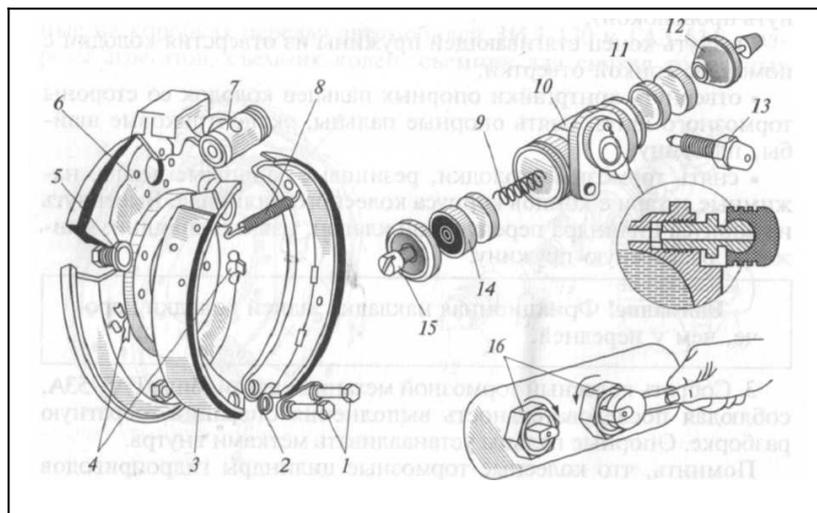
Колесный тормозной механизм (а) и колесный тормозной цилиндр (б) автомобиля ГАЗ-53А:
